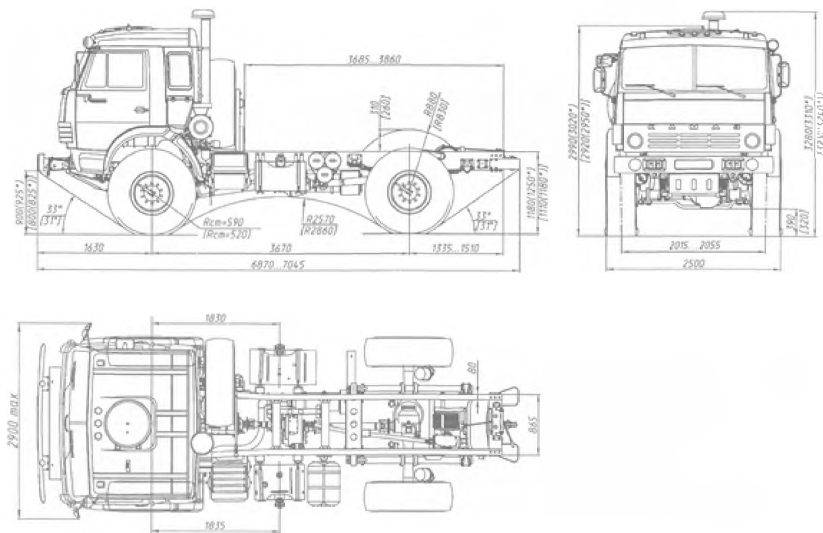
Шасси автомобиля-тягача КАМАЗ-43501. Габаритные размеры для автомобиля с шинами КАМА-1260 (КАМА-430).
